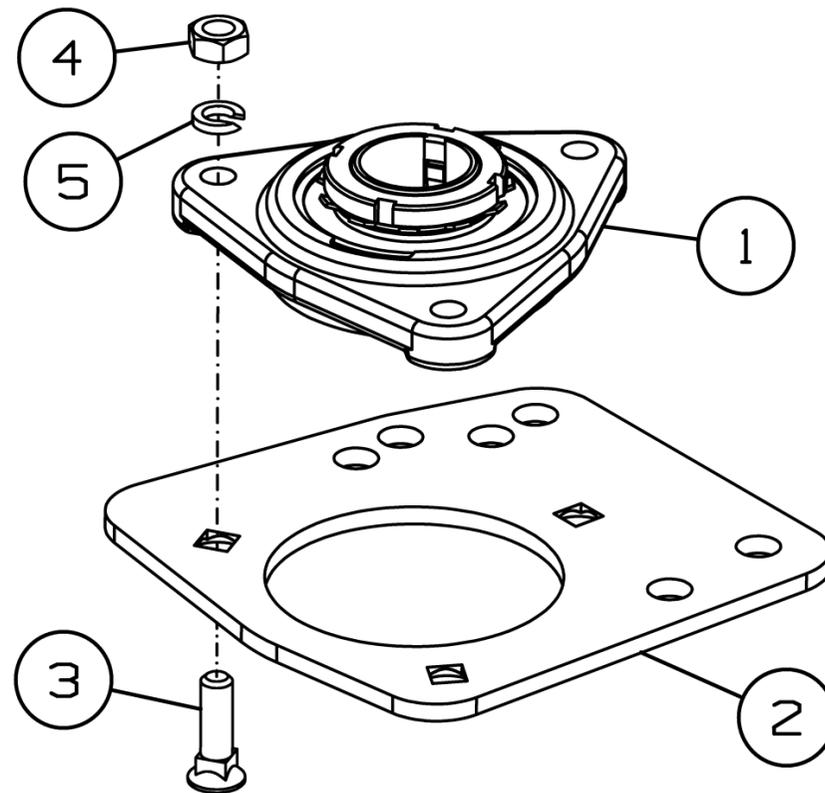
Корпус подшипника SS-780.01.06.140
